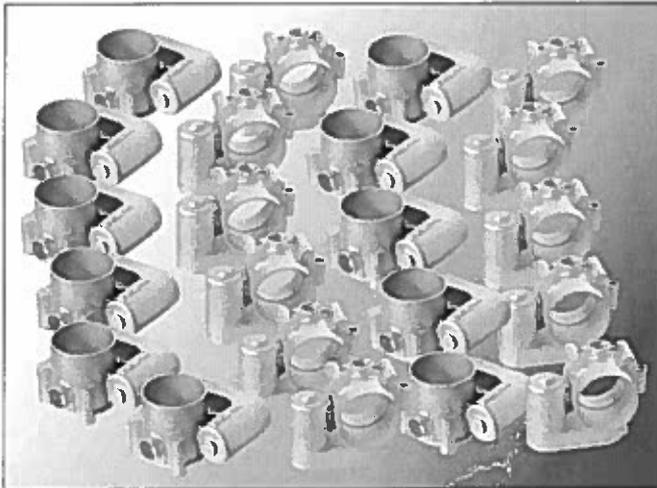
Elektrisch gesteuertes Ventilgehäuse für die Delphi-Studie, die nach dem MCP Metal Part Casting gefertigt wurden (Bild: MCP HEK Lübeck)
